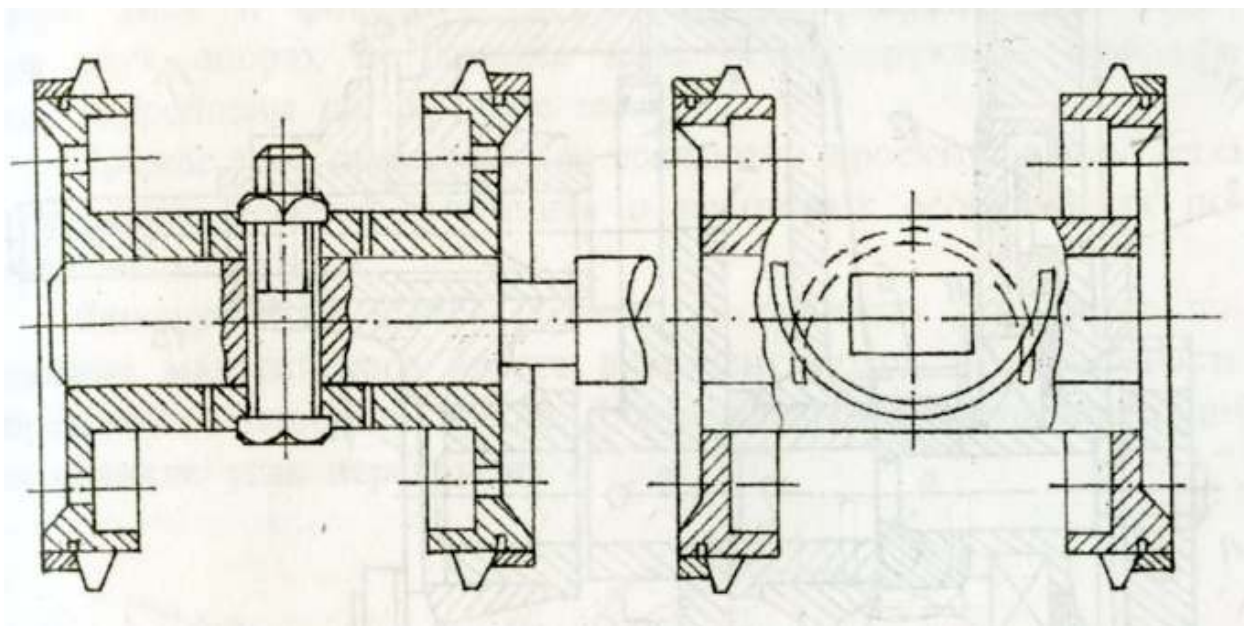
Способ крепления скачкового барабана с помощью винта и гайки
